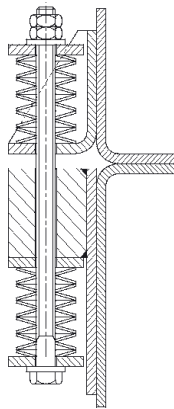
Lange Schrauben und Tellerfedern ESC-101
